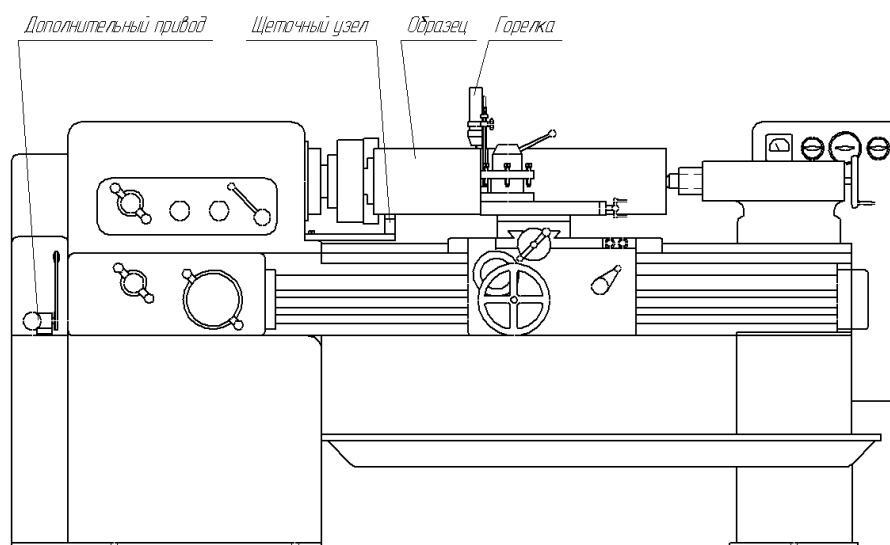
Экспериментальная установка на базе токарно-винторезного станка 1К62
